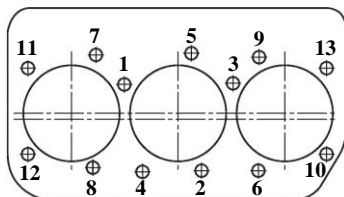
Схема затяжки болтов головки блока цилиндров
